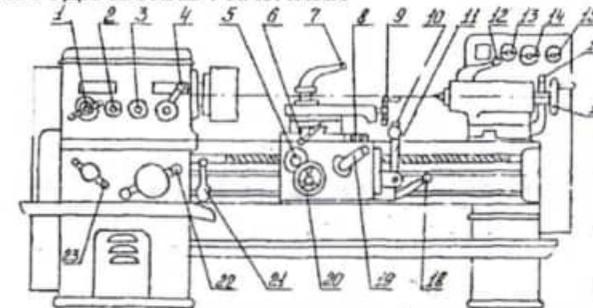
ОБЩИЙ ВИД СТАНКА
